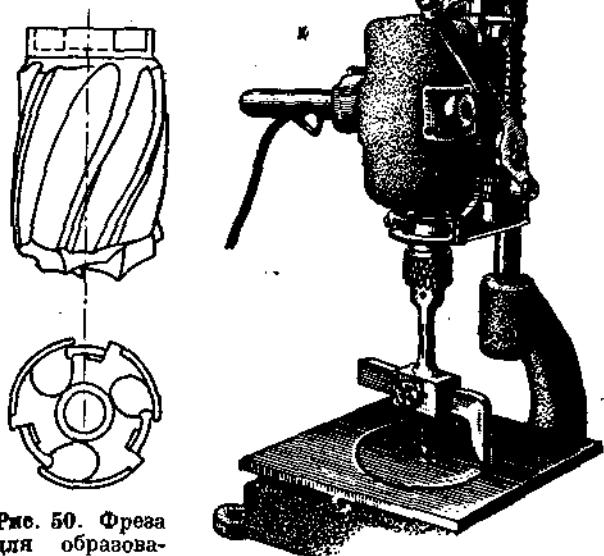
Фреза для образования отверстий для дымогарных труб.
